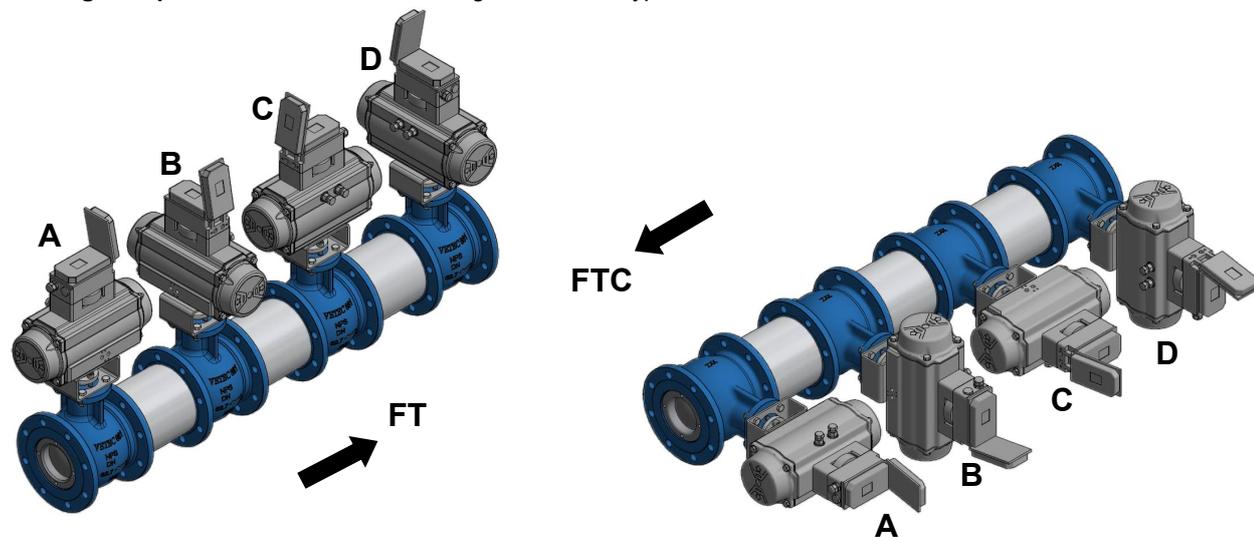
Stellventil Typ 62.7/AT • horizontale Einbaulage • Anbauarten des Antriebs auf den Ventil A, B, C, D
